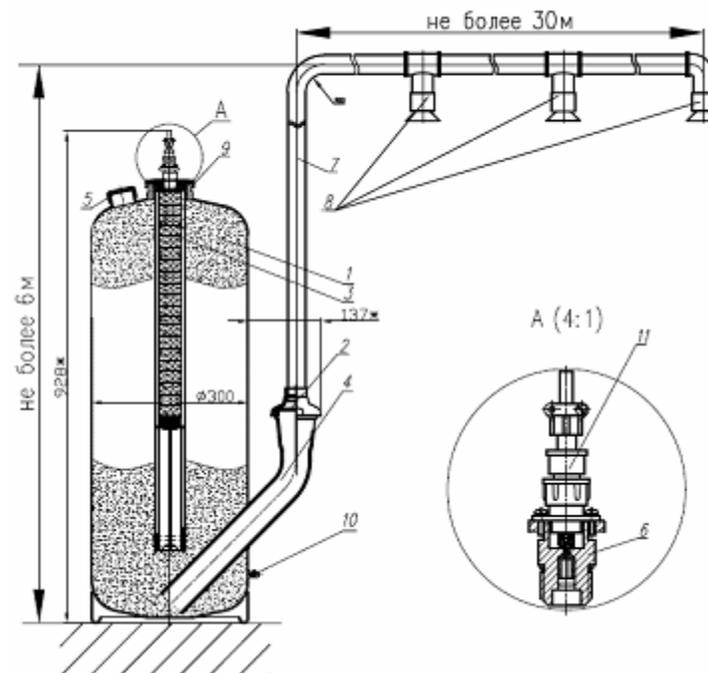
Схема модуля порошкового пожаротушения «БУРАН 50КД»: 1 - корпус с огнетушащим порошком; 2 - мембранный узел; 3 - генератор газа; 4 – горловина направляющая; 5 - засыпная горловина с заглушкой; 6 – электровоспламенитель; 7 - трубопровод подачи порошка; 8 - распылители; 9 - накидная гайка; 10- узел заземления (болт М6х12 (1шт.), гайка М6 (1шт.), шайба М6 гровер (1шт.), шайба М6 (2шт.)); 11- кабельная часть разъема
